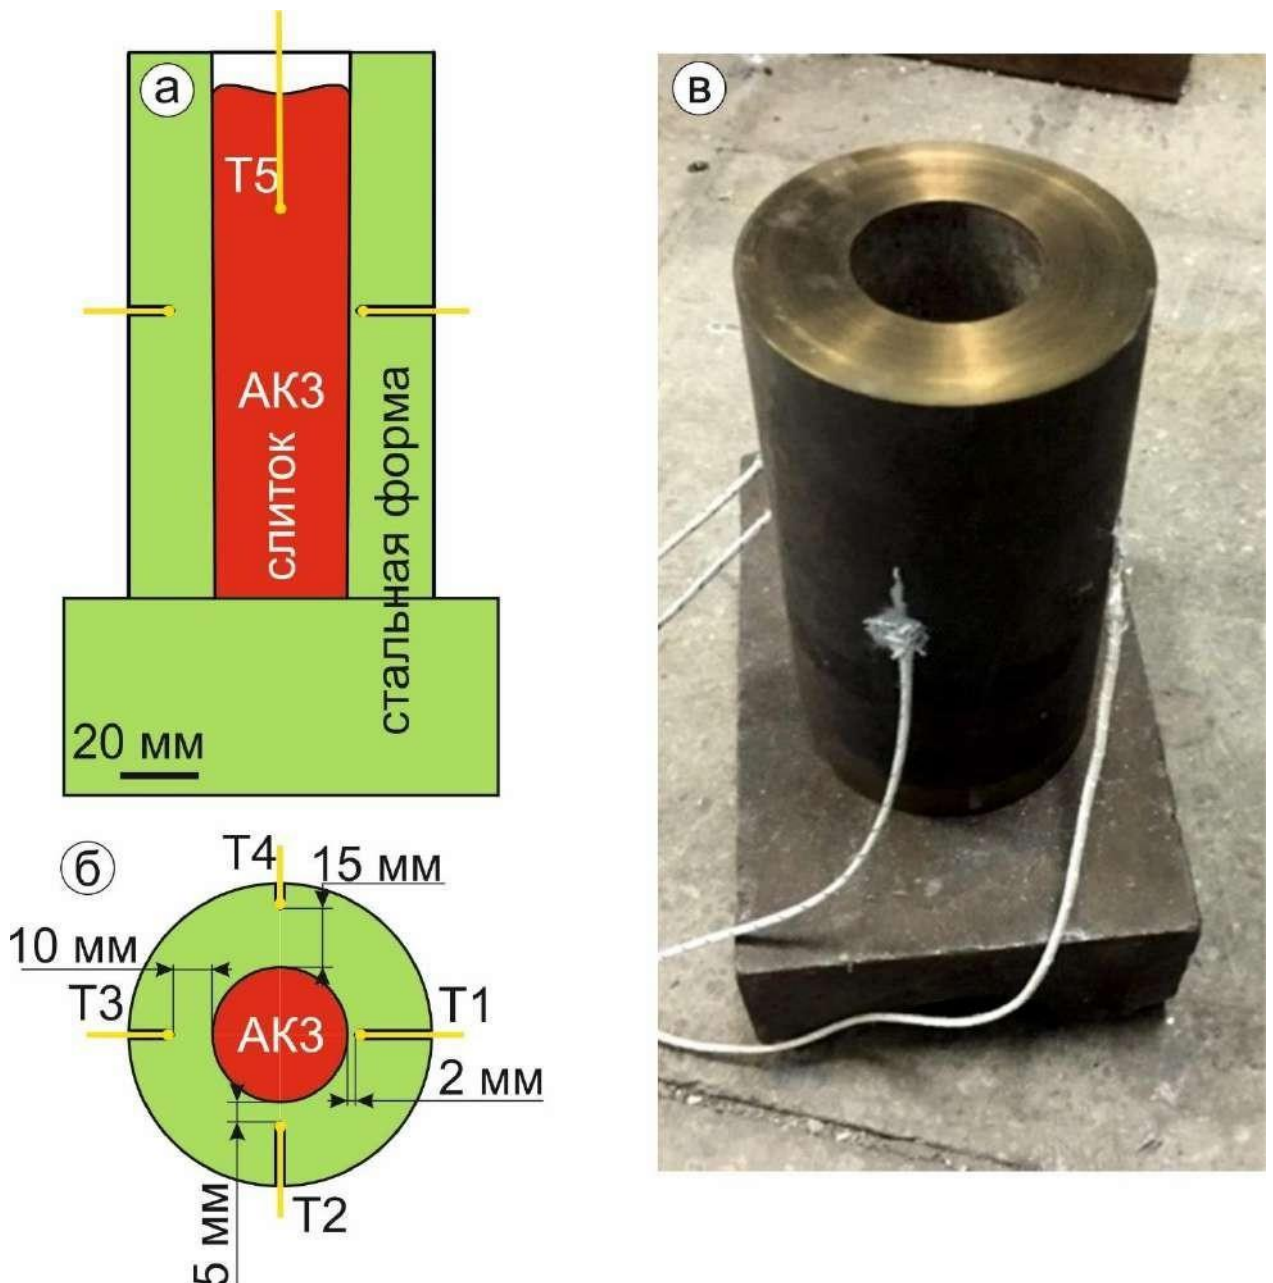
Схема розташування термопар у формі зі сталі Ст3 і загальний вигляд форми; а) форма в розрізі вид збоку; б) вид на форму зверху; в) загальний вигляд форми зі встановленими термопарами
